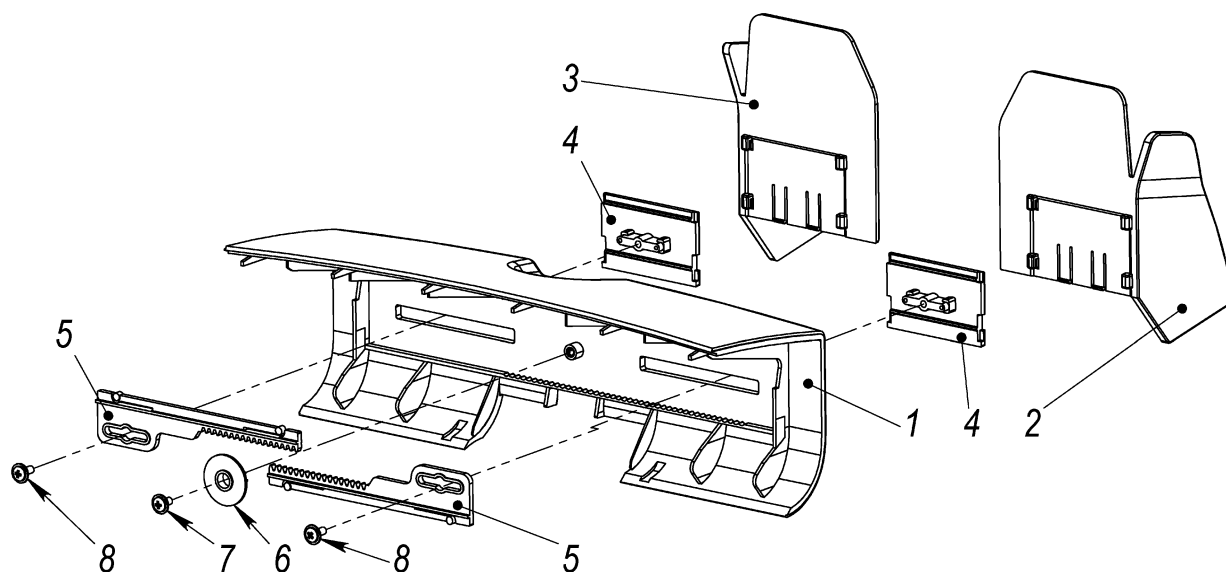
Узел крышки верхней в сборе ЕВКМ.00D800.02.13.000
